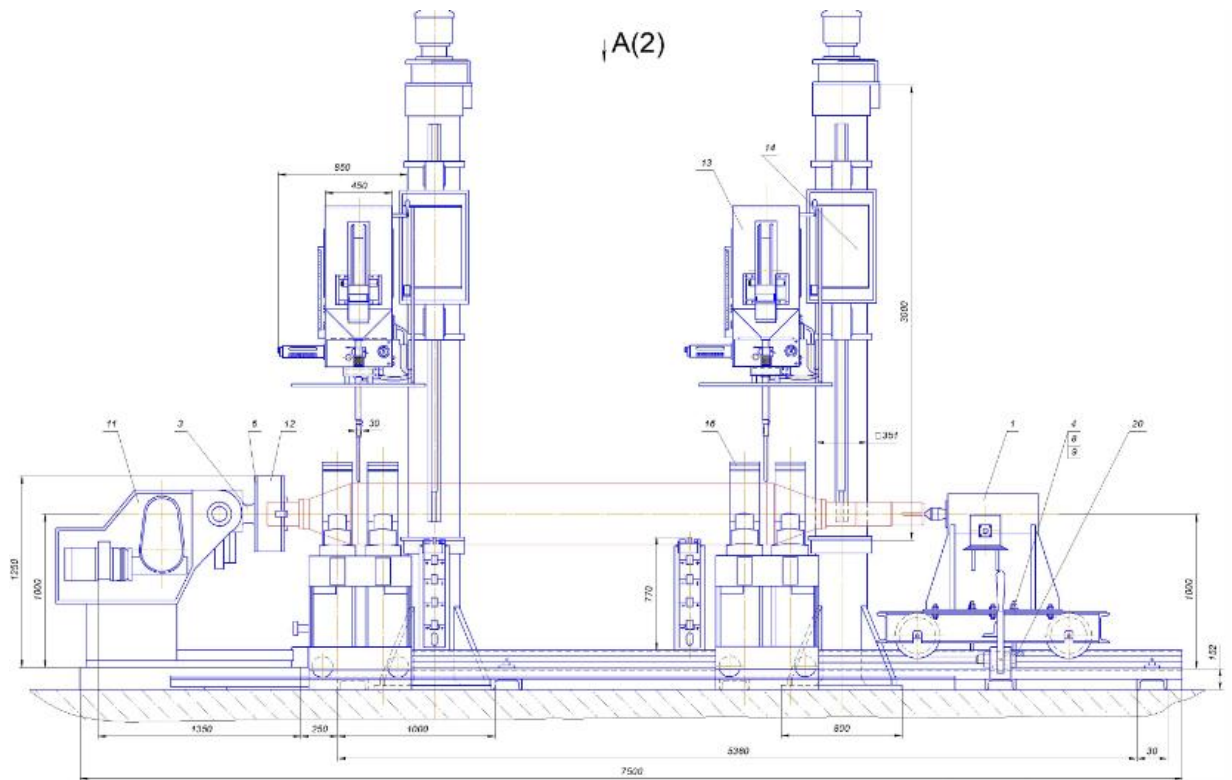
Установка для наплавлення під флюсом валків прокатних станів
